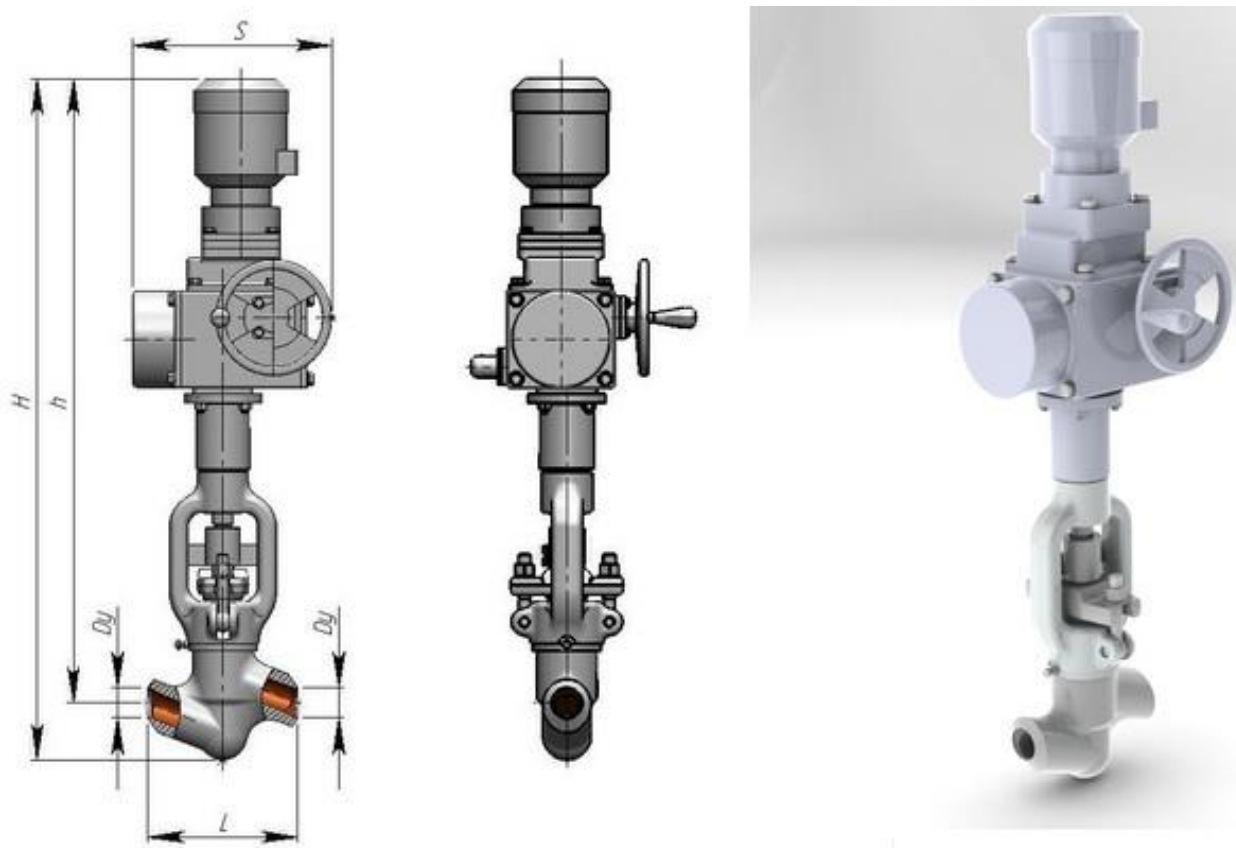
Внешний вид клапана 9с-5-4Э
